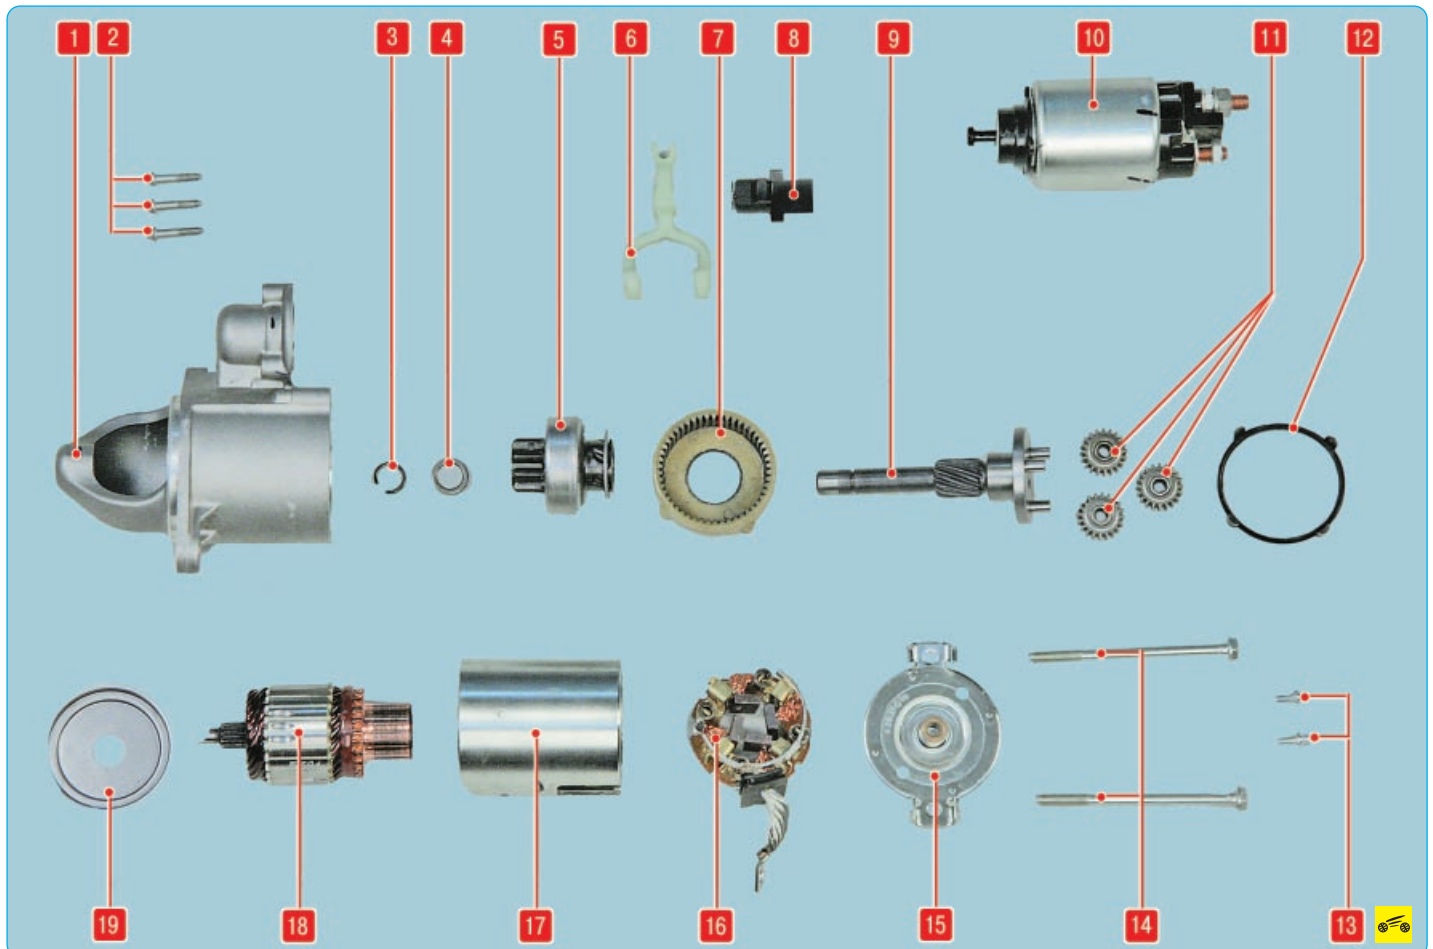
Детали стартера: 1 – крышка со стороны привода; 2 – винты крепления тягового реле к крышке со стороны привода; 3 – стопорное кольцо муфты привода; 4 – упорное кольцо муфты привода; 5 – муфта привода; 6 – рычаг привода; 7 – коронная шестерня; 8 – опора рычага привода; 9 – вал привода; 10 – тяговое реле; 11 – сателлиты; 12 – уплотнительное кольцо планетарного редуктора; 13 – болты крепления крышки со стороны коллектора; 14 – стяжные болты; 15 – крышка со стороны коллектора; 16 – щеточный узел; 17 – статор; 18 – ротор; 19 – крышка планетарного редуктора
